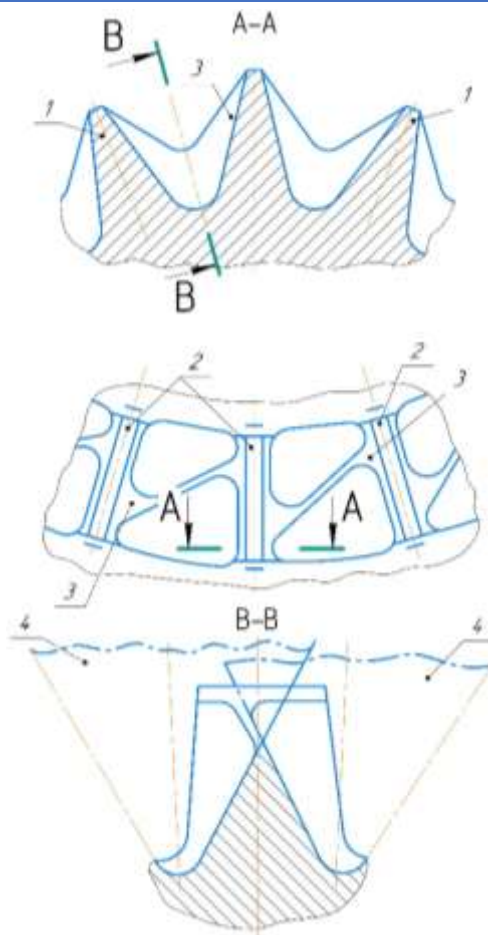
Фрезерованные зубья на венцах шарошек с наклонными остроугольными перемычками.
